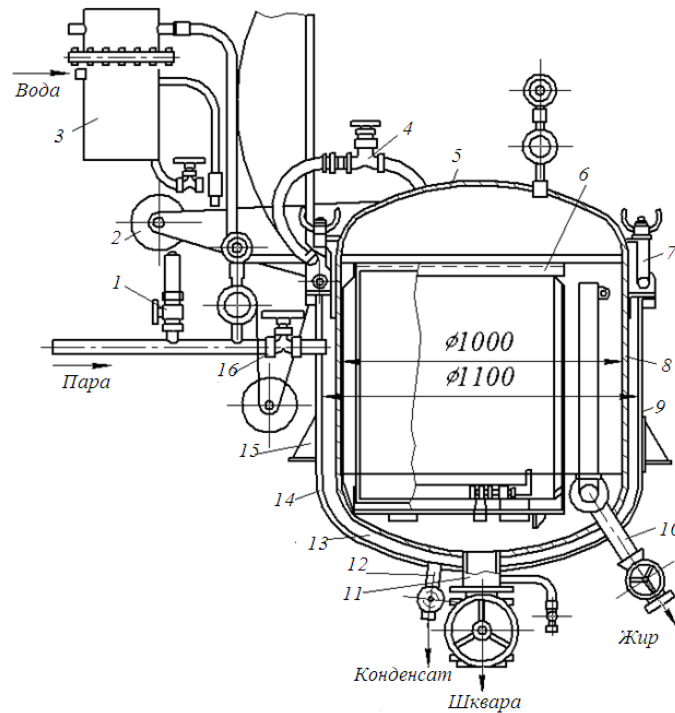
Автоклав для витоплювання жиру: 1 – запобіжний клапан; 2 – противага; 3 – конденсатор; 4 – клапан; 5 – еліптична кришка; 6 – кошик; 7 – відкидні болти, 8 – внутрішній корпус; 9 – зовнішній корпус; 10 – патрубок для зливання жиру; 11 – труба для відведення шквари; 12 – труба для зливання конденсату; 13, 14 – еліптичні днища внутрішнього і зовнішнього корпусів; 15 – опорні лапи; 16 – клапан паропроводу
